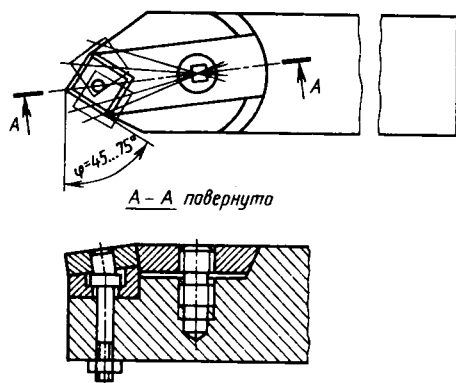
Конструкция резца, обеспечивающая изменения главного угла в плане
